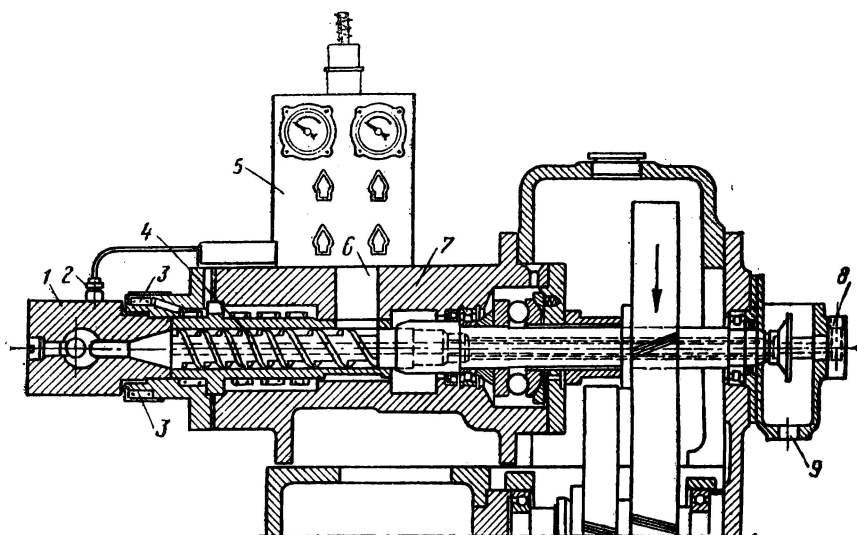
Разрез рабочей части червячного пресса для наложения пластмассовой изоляции на провод
